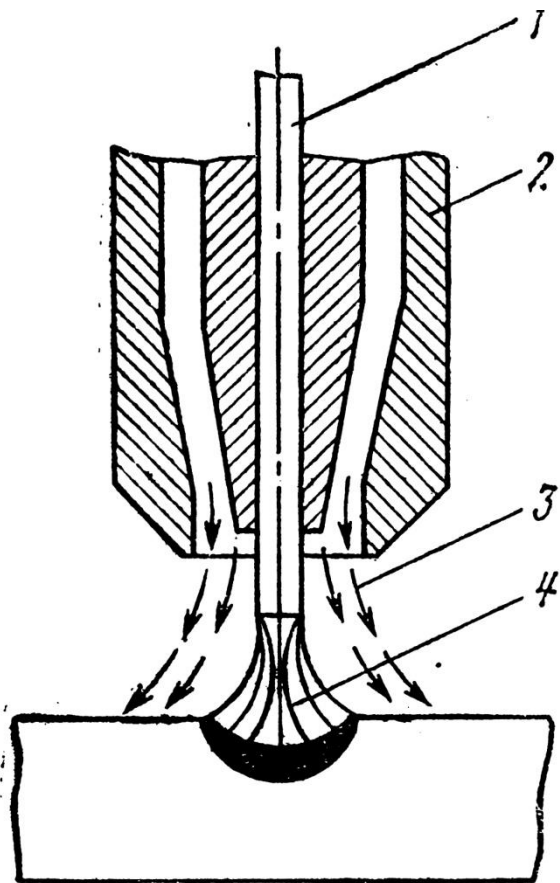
Схема процесса сварки в защитной среде углекислого газа:
